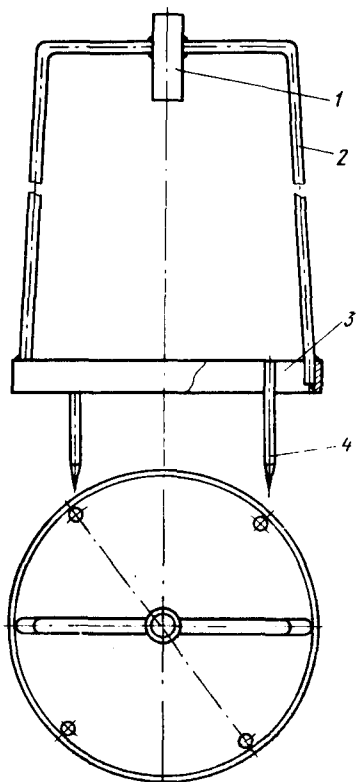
Неподвижный узел трехножевого устройства для обрезки кустов земляники:
